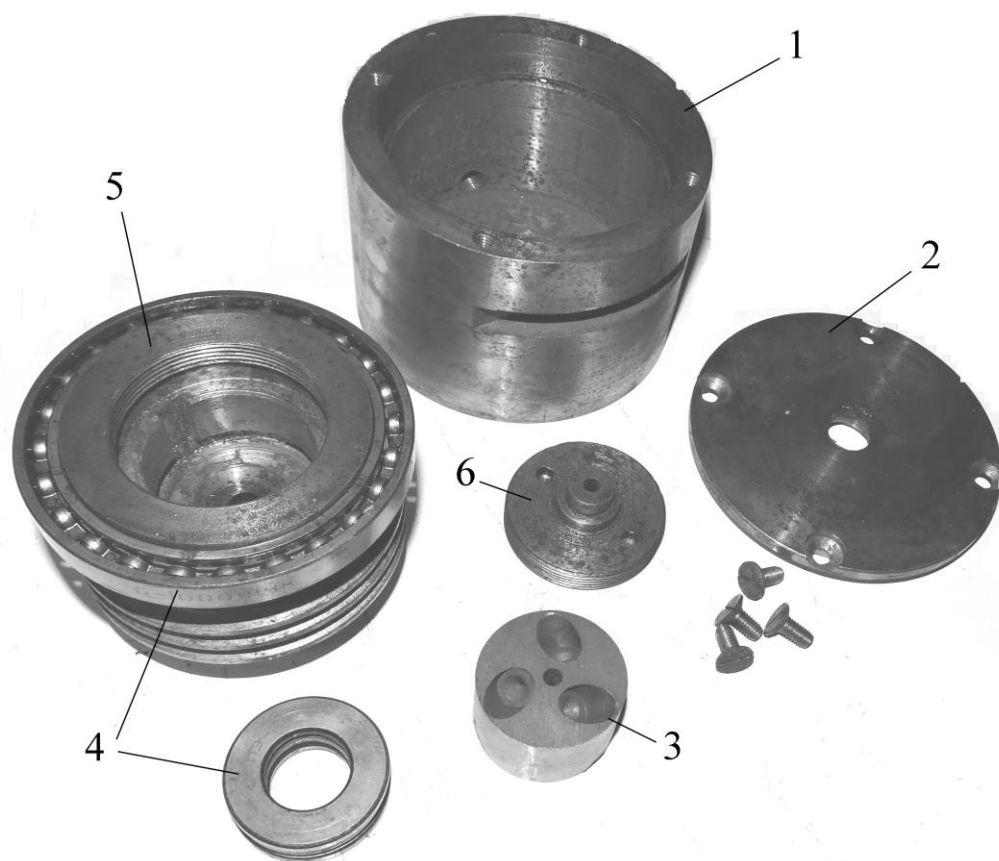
Детализовка сборной волоки для получения винтовых профилей
